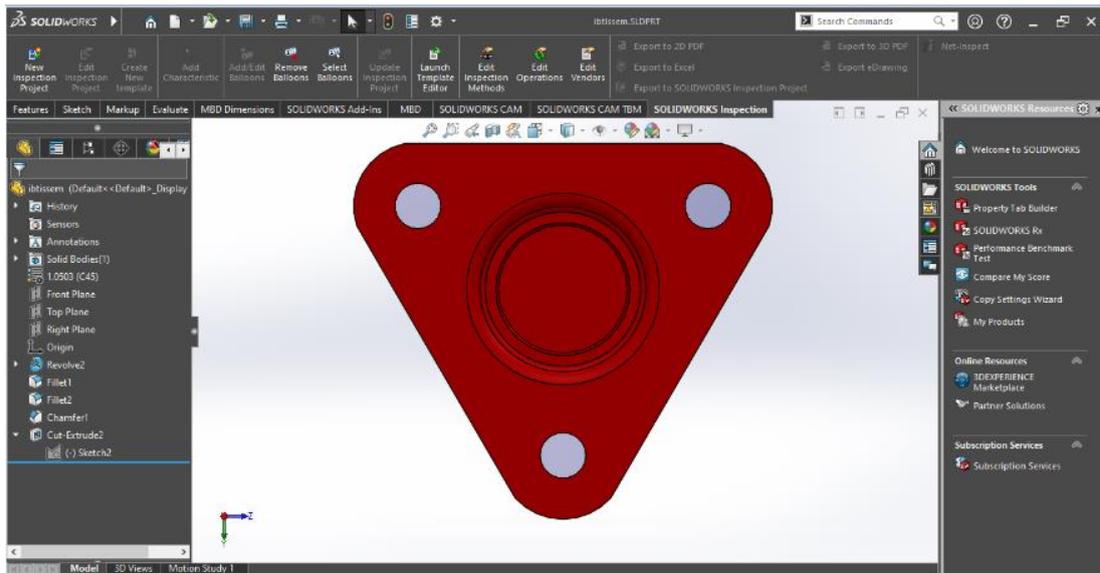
pièce finie d'axe de roue sur SolidWorks
